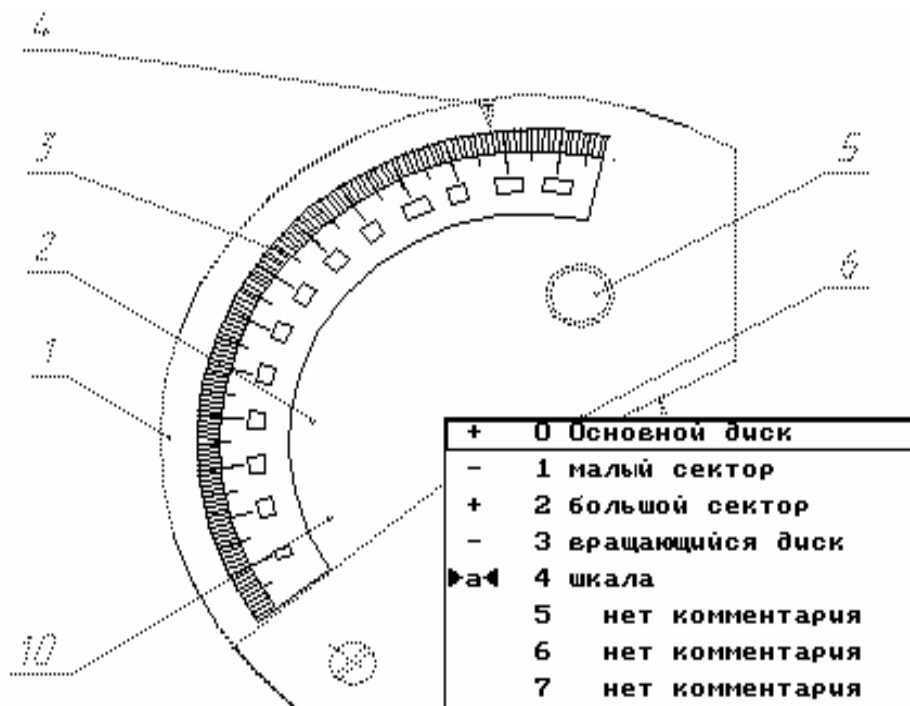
Фрагмент сборочного чертежа угломера с различным статусом слоев
